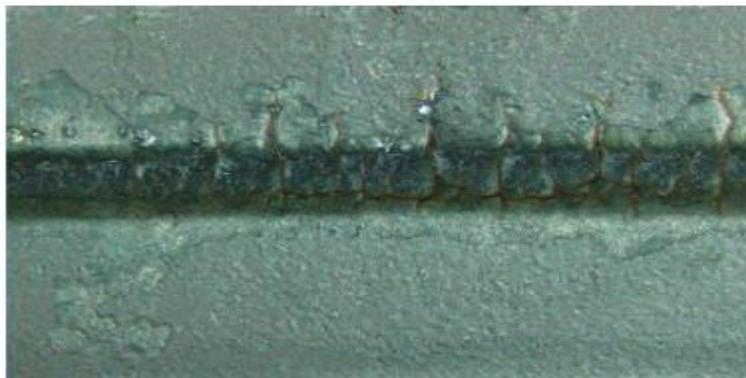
6 Grietas en material de molde por fatiga térmico Fuente: Revista de Metalurgia
